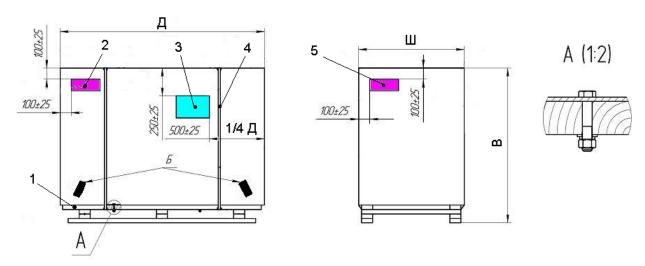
Упаковочный гофроящик установки: 1 — поддон; 2 и 5 — наклейки «Манипуляционные знаки»; 3 — наклейка «Транспортная маркировка»; 4 — клеевая лента; Б — наклейка «Места строповки».
